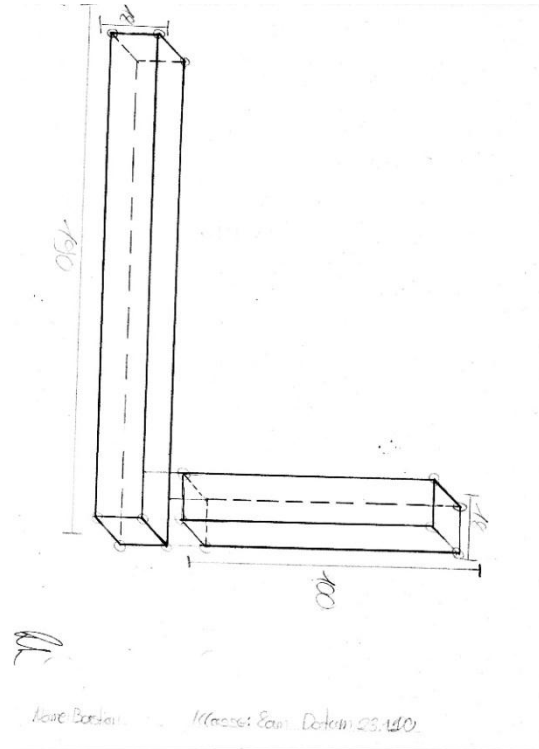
Stumpfe Verbindung; Explosionszeichnung
